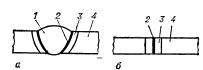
Сварное соединение: 1 — сварной шов; 2 — зона сплавления (а) или соединения при сварке давлением (б); 3 — зона термического влияния; 4 — прилегающий основной материал.
